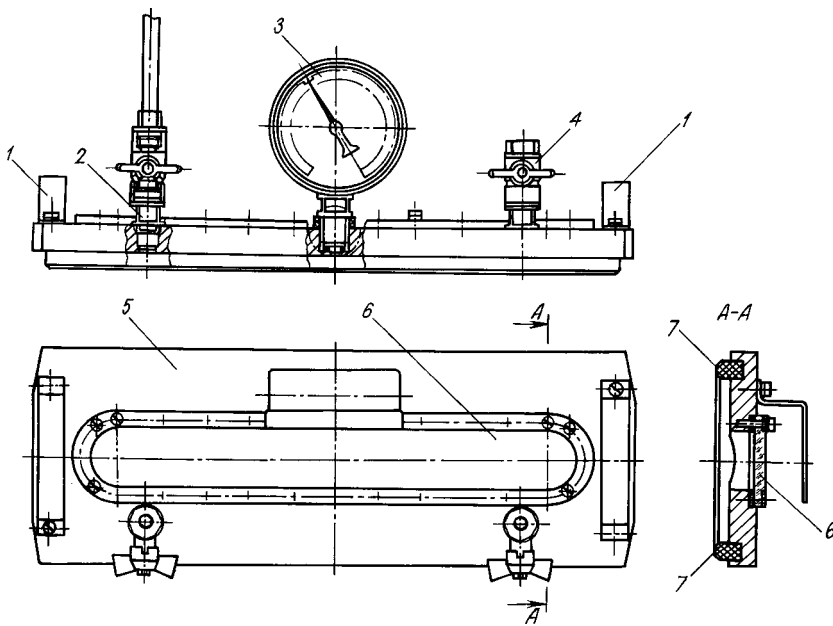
Конструктивная схема вакуумной камеры, разработанной ЦНИИТС: 1 — ручки; 2 — штуцер для отвода воздуха; 3 — мановакуумметр; 4 — штуцер для подачи воздуха; 5 — корпус; 6 — смотровое окно из оргстекла; 7 — резиновое уплотнение
